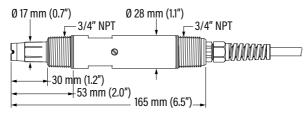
HI7640-18zz sonda de OD galvánica con cable acoplado
